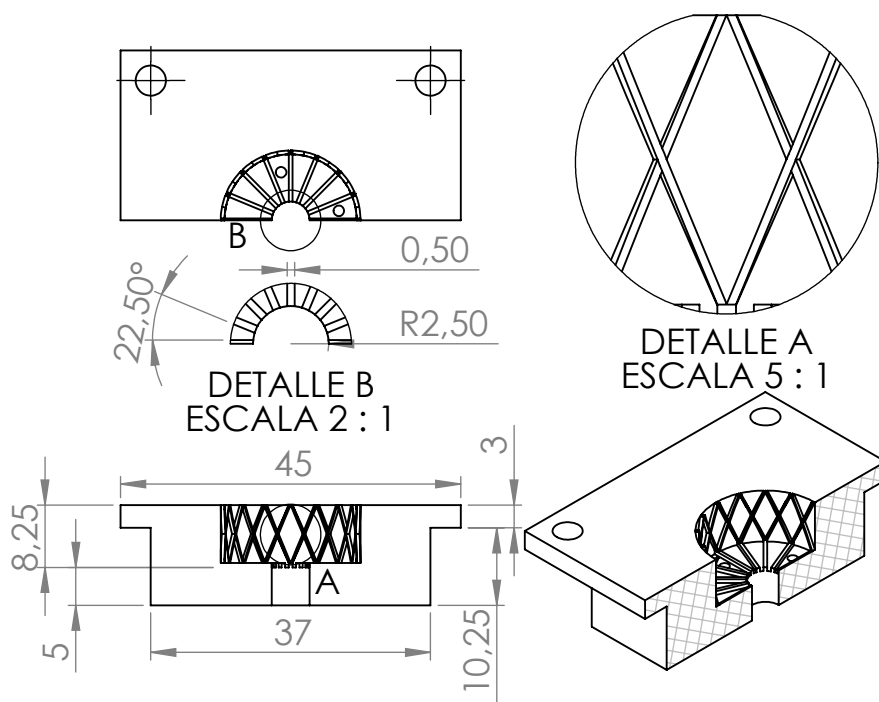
Vista en corte del molde del *Robot Biaxial* parte B
